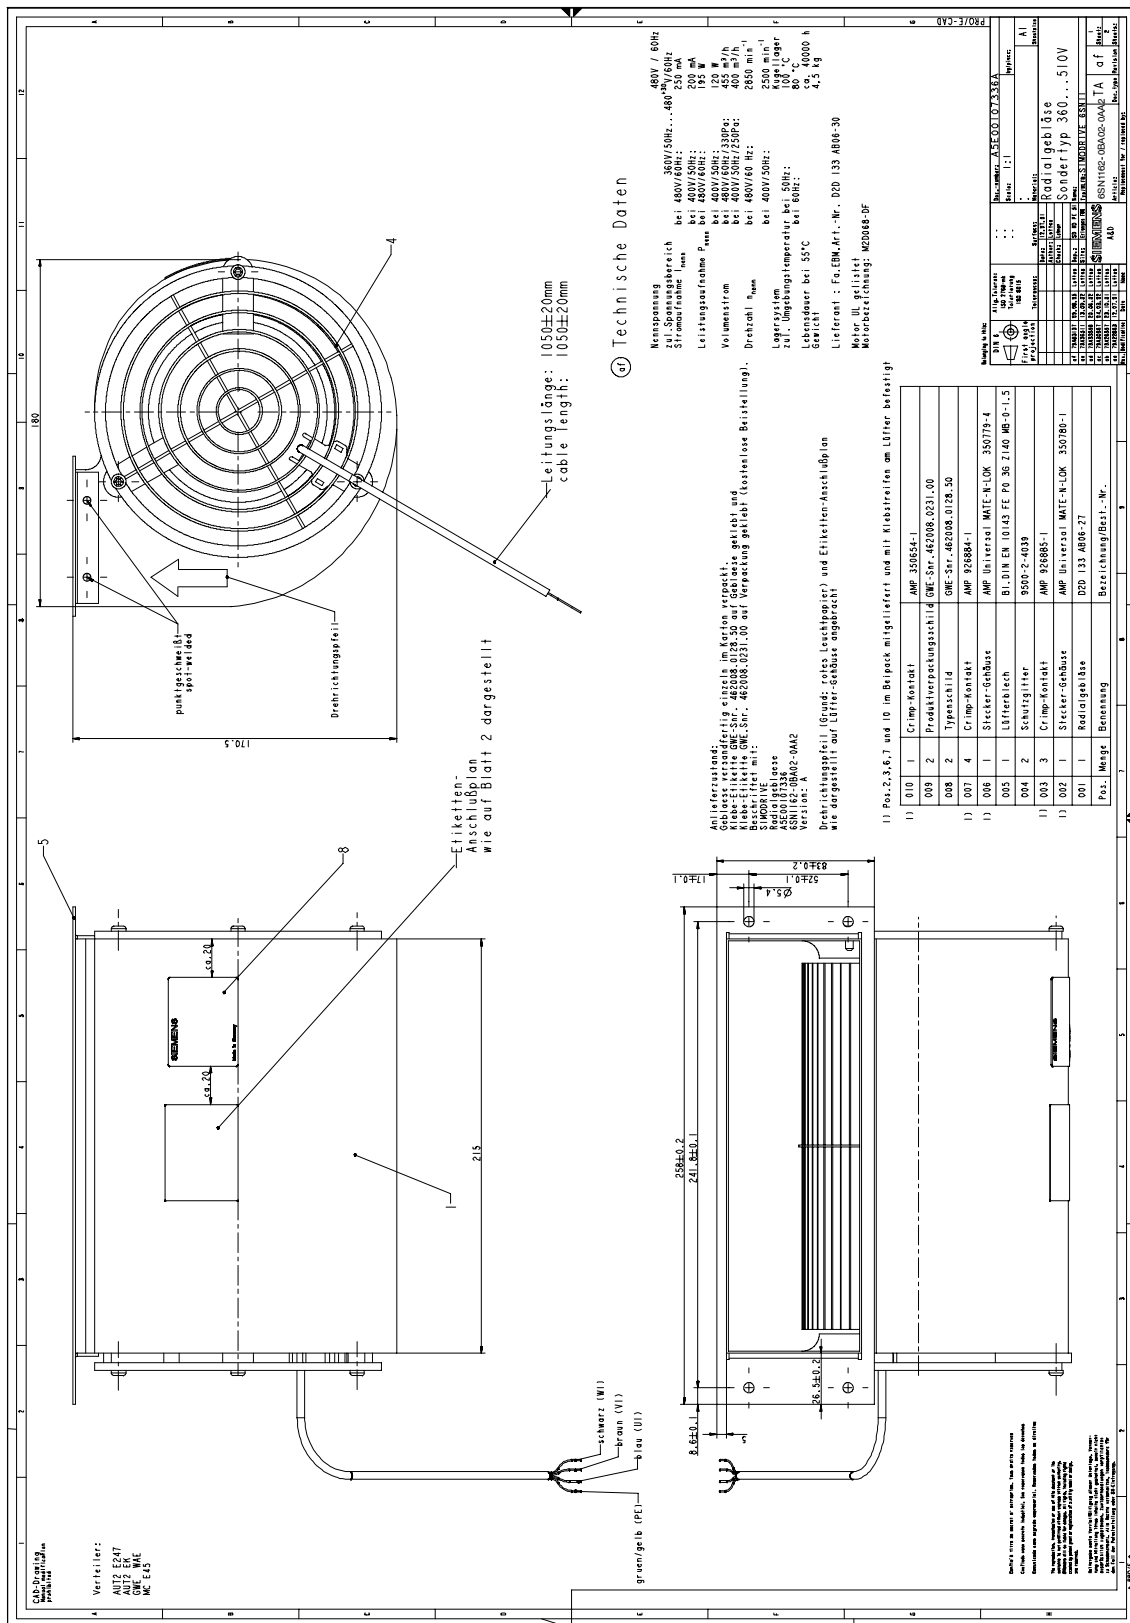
Ventilateur rapporté, 6SN1162-0BA02-0AA2; plan d'encombrement
